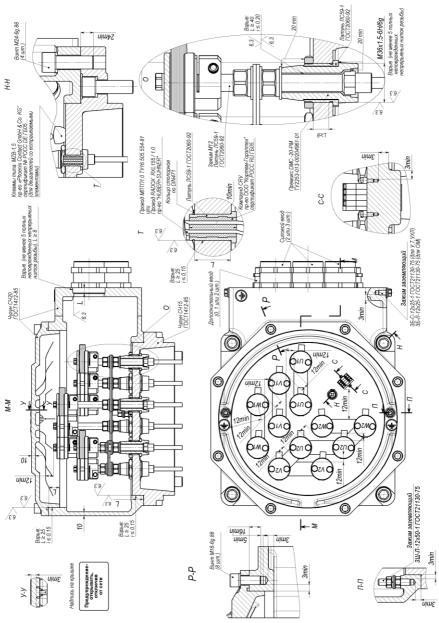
Чертеж взрывозащиты коробки выводов «d» двигателей ВА(Б),1РВА 355, BRA(Б),1РВКА 355
